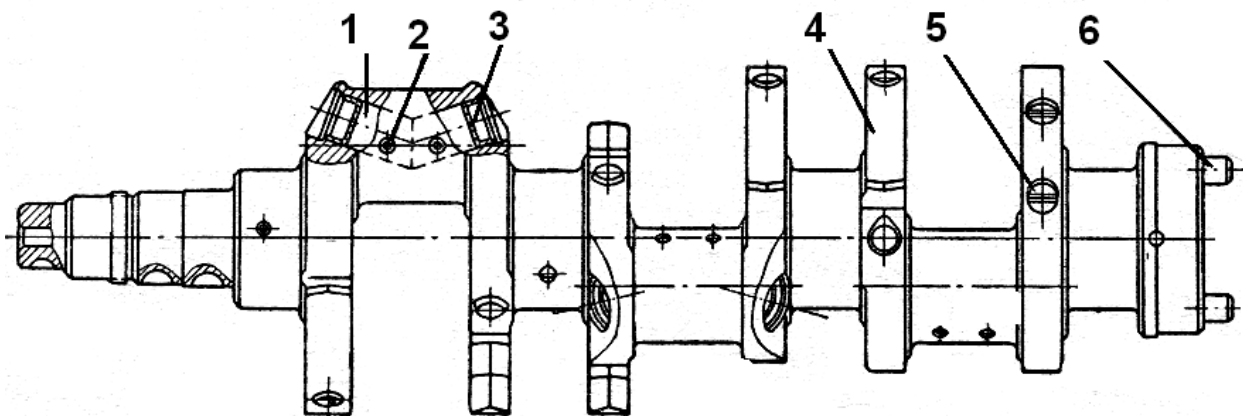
Коленчатый вал ЯМЗ-236:
